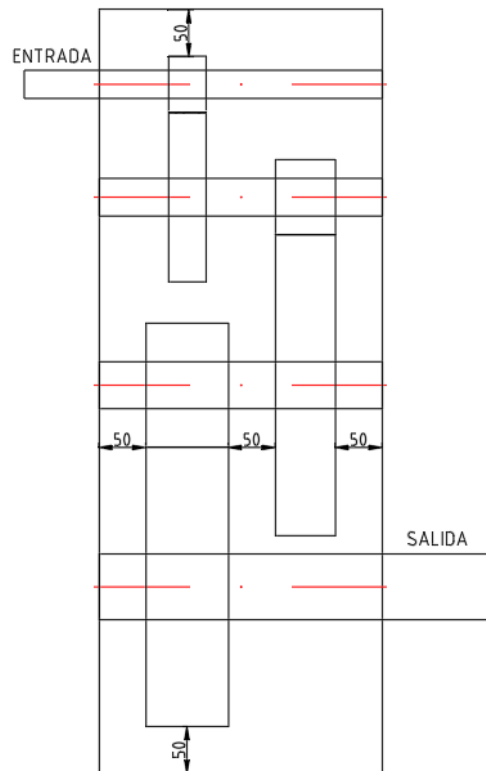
Vista en planta de la disposición de la caja reductora y distancias.
